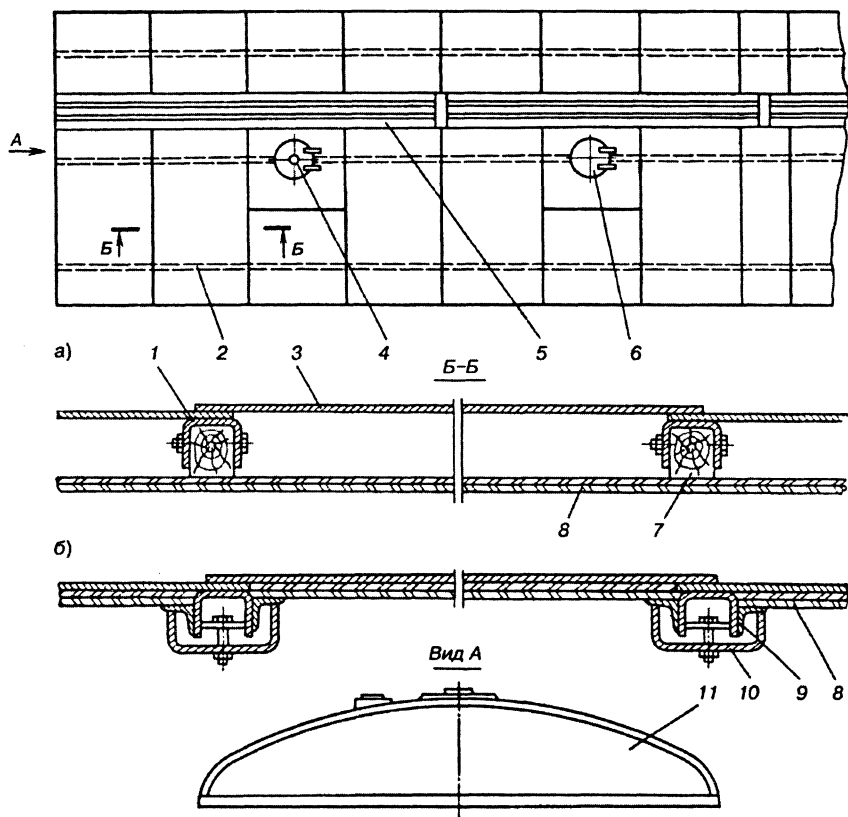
Крыша универсального крытого вагона со старым (а) и новым (б) способами укладки и крепления подшивки
